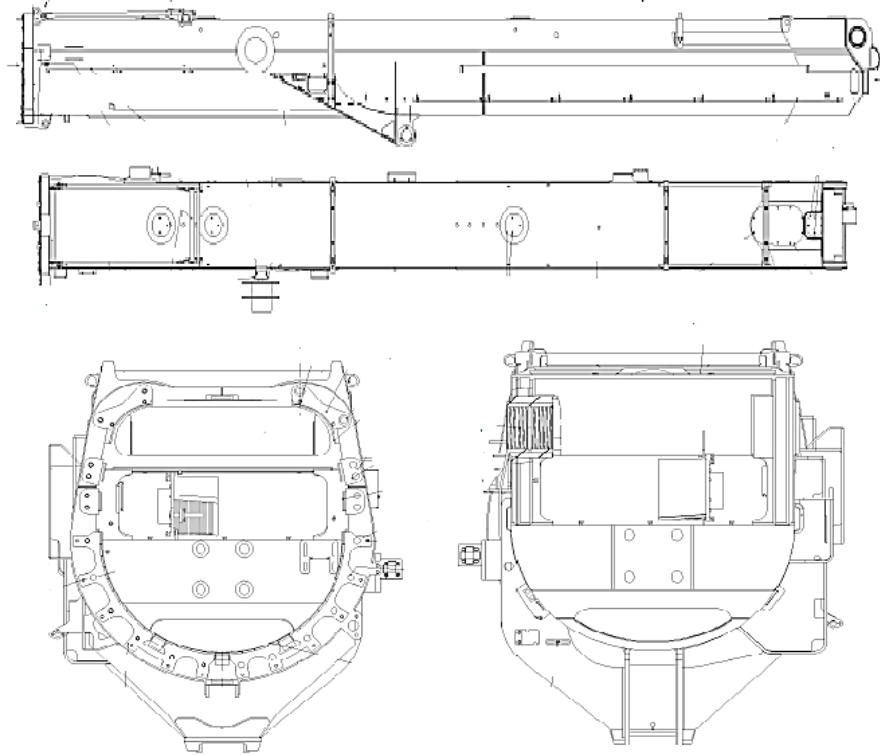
Pie de Pluma vista lateral, frontal y posterior
